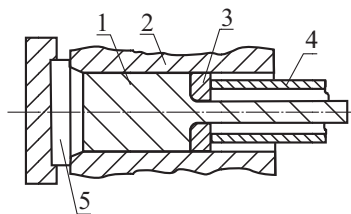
Схема обратного прессования прутков: 1 – заготовка (слиток); 2 – контейнер; 3 – инструмент (матрица); 4 – пресс-штемпель; 5 – заглушка
